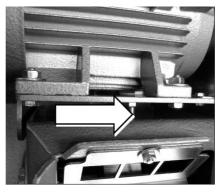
Keilriemen-Spannschraube zwischen Motorplatte und Maschinengehäuse
